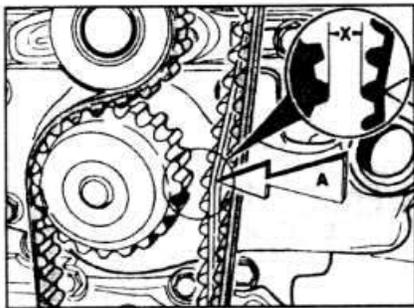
В.15. Проверка натяжения зубчатого ремня.
